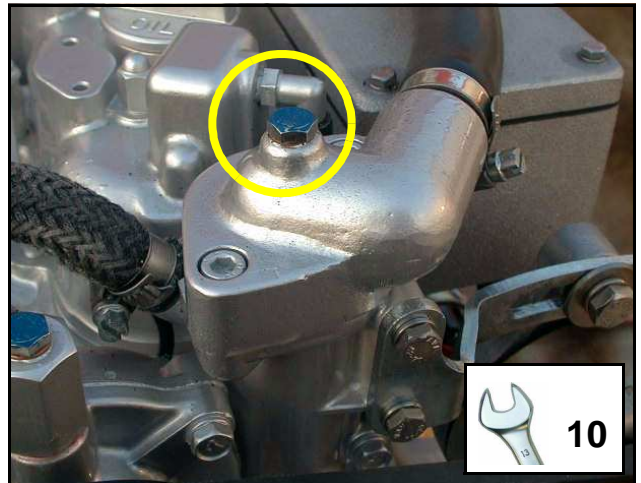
Entlüftungsschraube am Thermostatgehäuse
